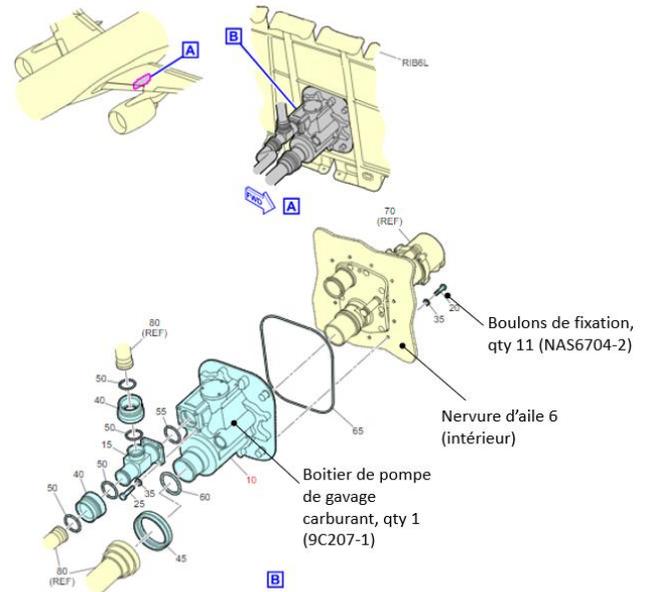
Ensemble de boîtier de pompe de gavage carburant et de nervure d'aile 6 côté gauche
